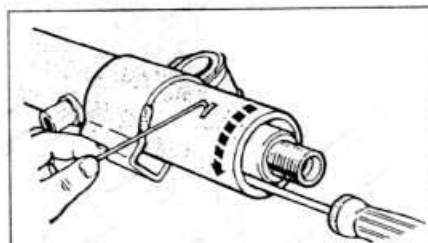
Снятие стопорного кольца опорной втулки рейки при разборке рулевого механизма Cam Gears
